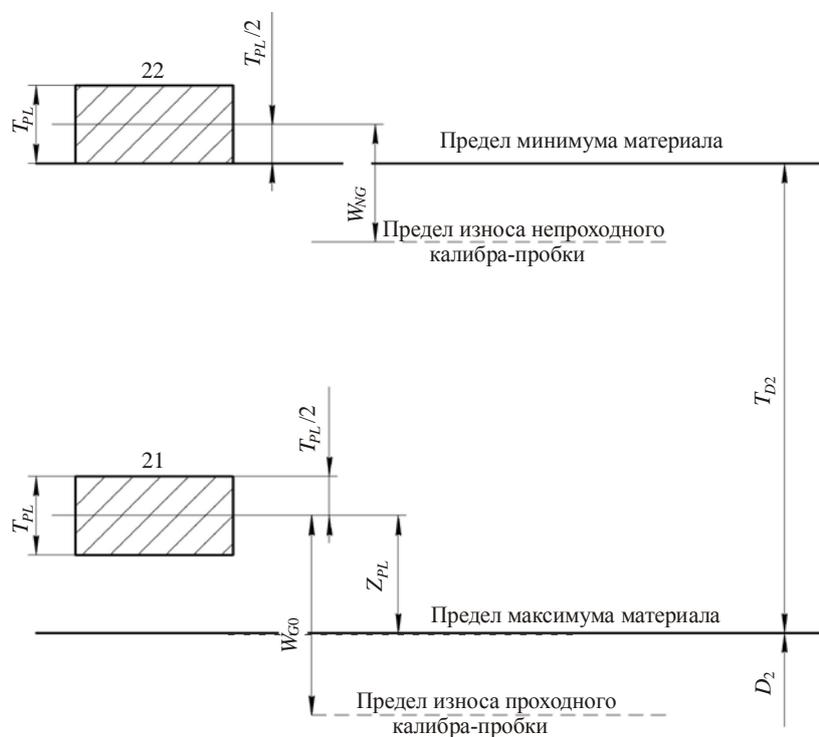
Расположение полей допусков среднего диаметра резьбовых калибров для внутренней трапецеидальной резьбы
